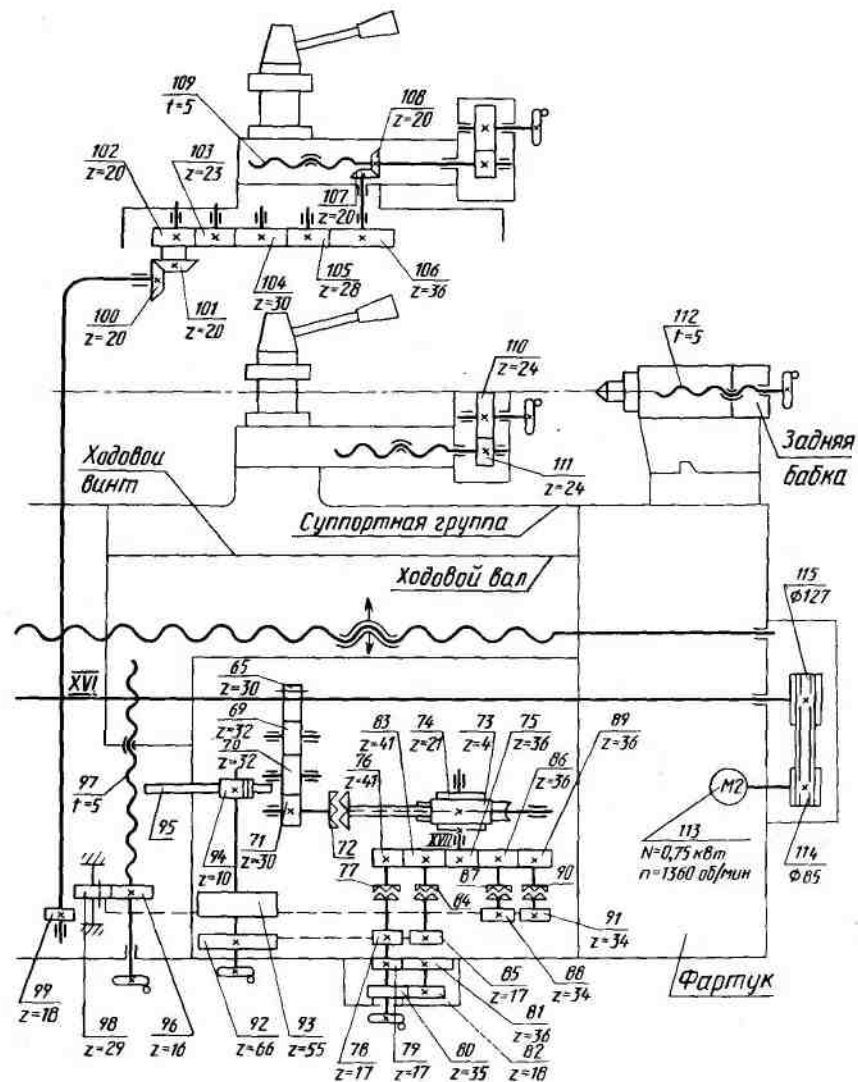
Кинематическая схема суппортной группы и фартука токарно-винторезного станка мод. 16K20
